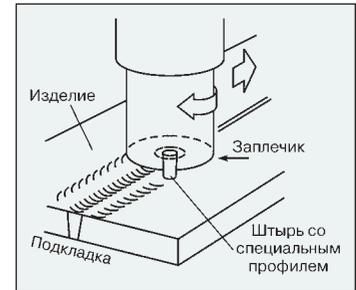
Схема процесса сварки трением с перемешиванием
